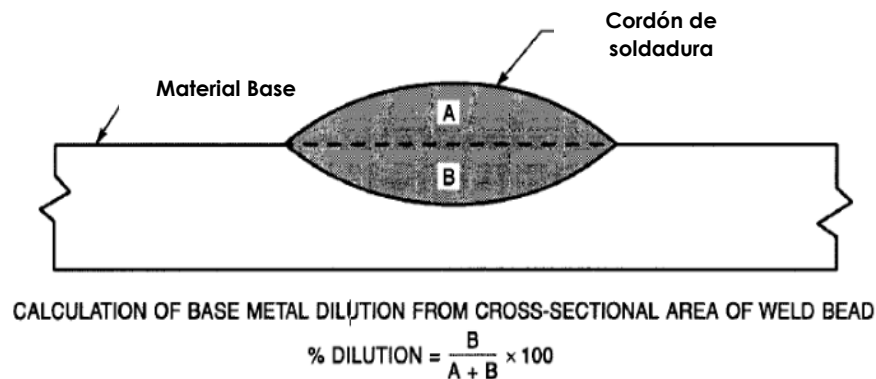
Cálculo de dilución de soldadura conforme a AWS 3.0 (American Welding Society, 2010).
